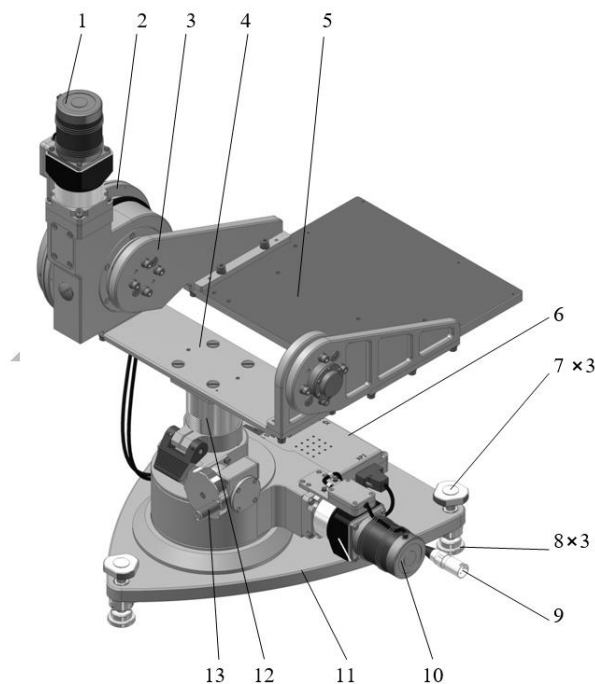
Общий вид стола наклонно-поворотного: 1 – шаговый двигатель; 2 – абсолютный датчик угла поворота; 3 – кронштейн; 4 – плита; 5 – установочная платформа; 6 – блок управления; 7 – винт регулировочный; 8 – опора; 9 – сетевая кабель «+27V»; 10 – шаговый двигатель; 11 – основание; 12 – рейка; 13 – ручка
